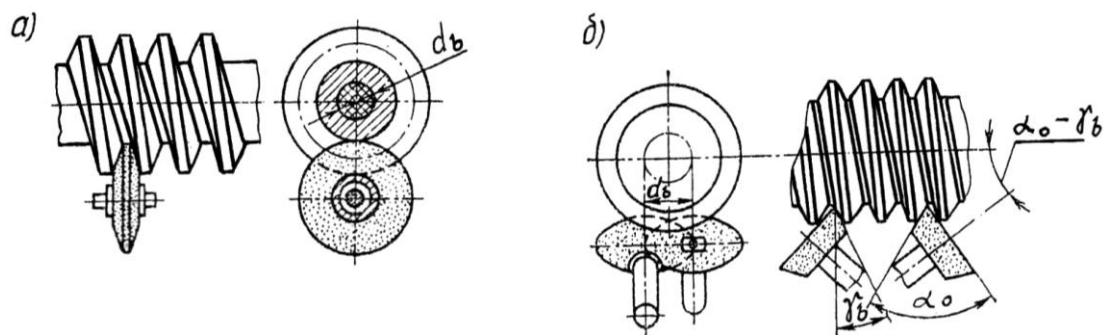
Схемы установки шлифовальных кругов при шлифовании эвольвентных червяков ZJ:
